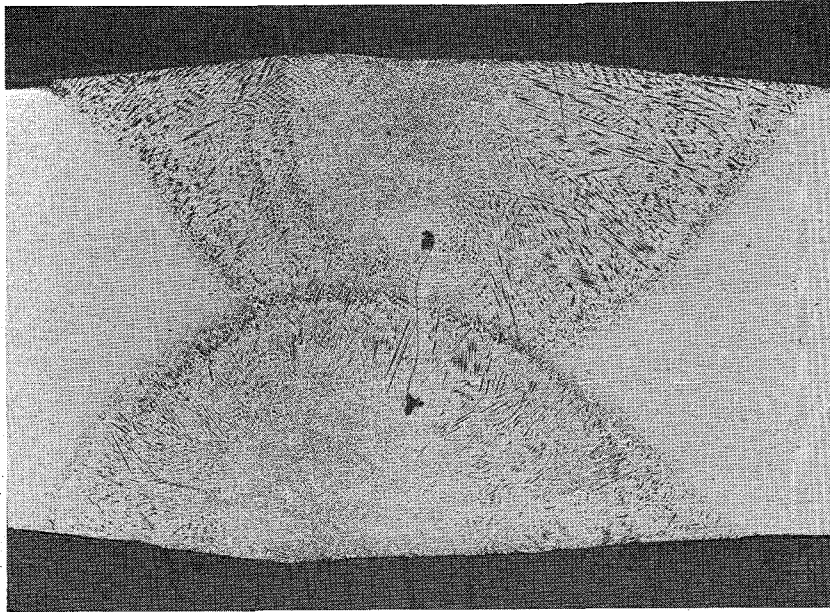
Makroaufnahme vom Querschliff der Schweißnaht bei Inconel 625 im WS-Zustand (Bindefehler aufgrund nicht entfernter Zunderschichten nach der Wärmebehandlung) $V = 16:1$
